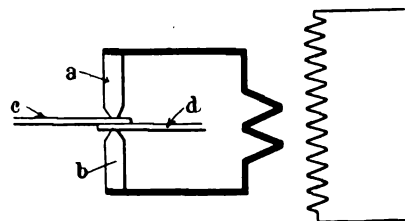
Principe de la soudure par recouvrement.
